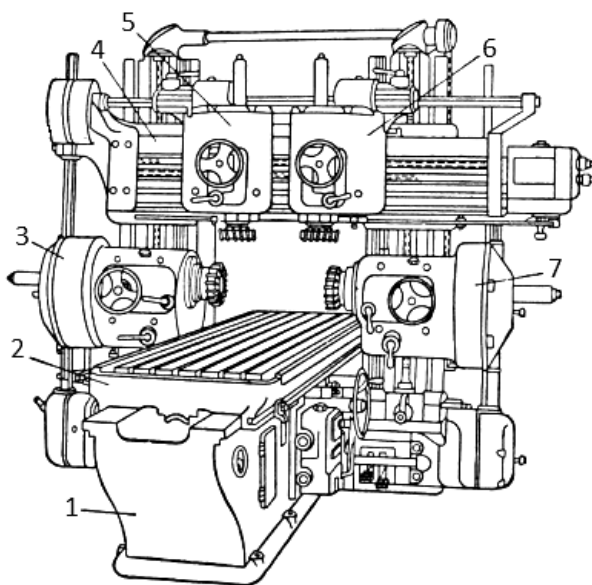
Поздовжньо-фрезерний верстат:
